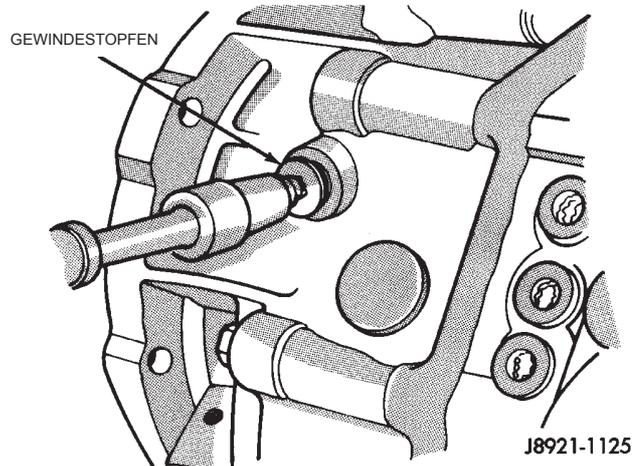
Gewindestopfen der Sperrkugel ausbauen
